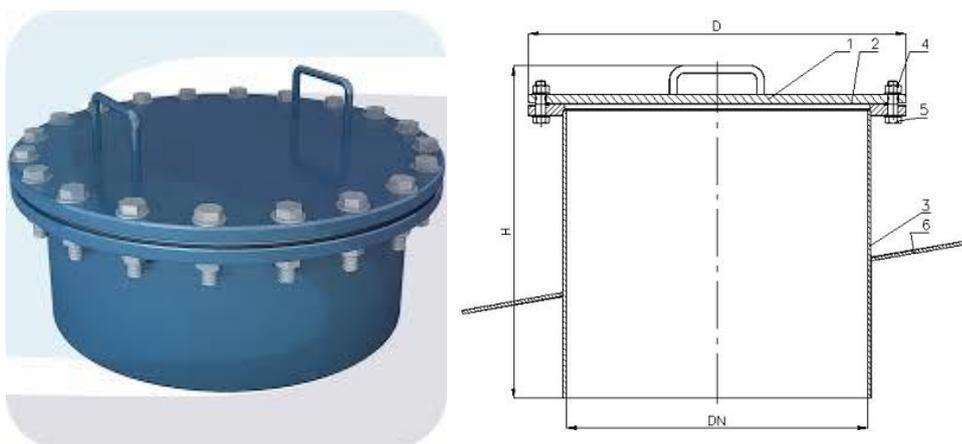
Световой люк ЛС-500. Изображение (слева) и общий вид (справа), [163]: 1 – крышка; 2 – прокладка; 3 – корпус; 4 – гайка; 5 – болт; 6 – усиливающая накладка
